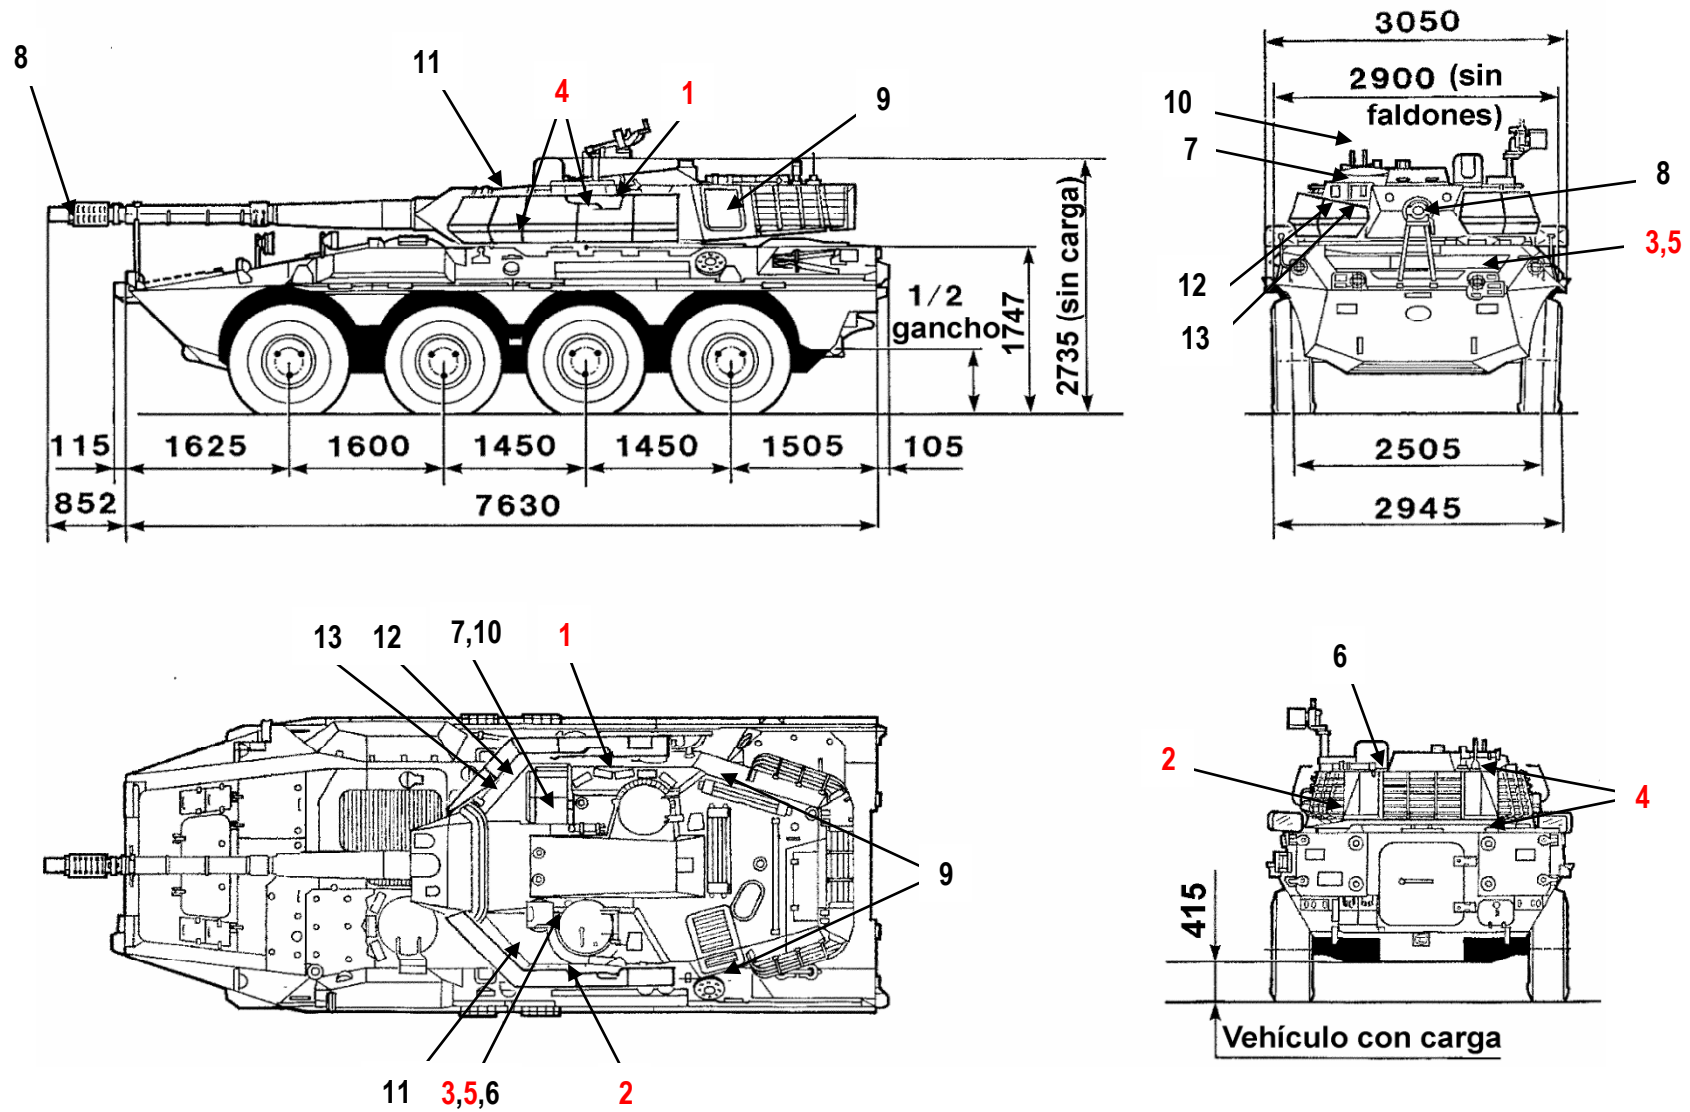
Planta, perfil y alzado del VRCC Centauro con posible distribución de componentes del DSS
